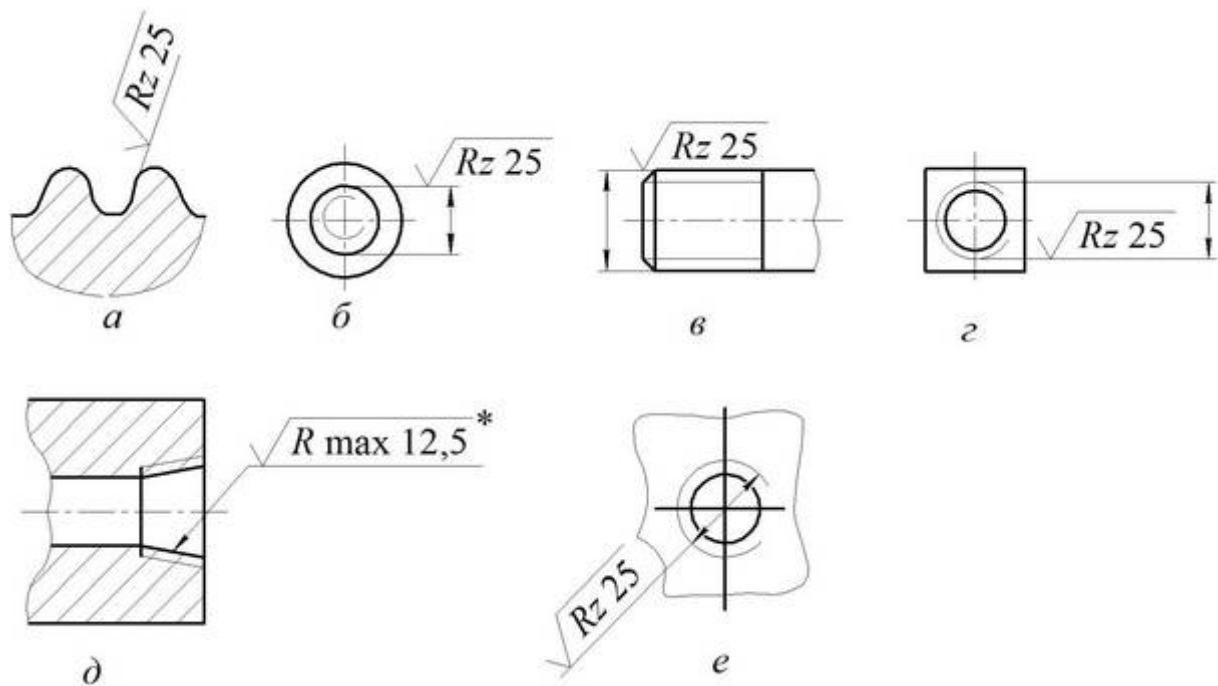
Обозначение шероховатости поверхности профиля резьбы
